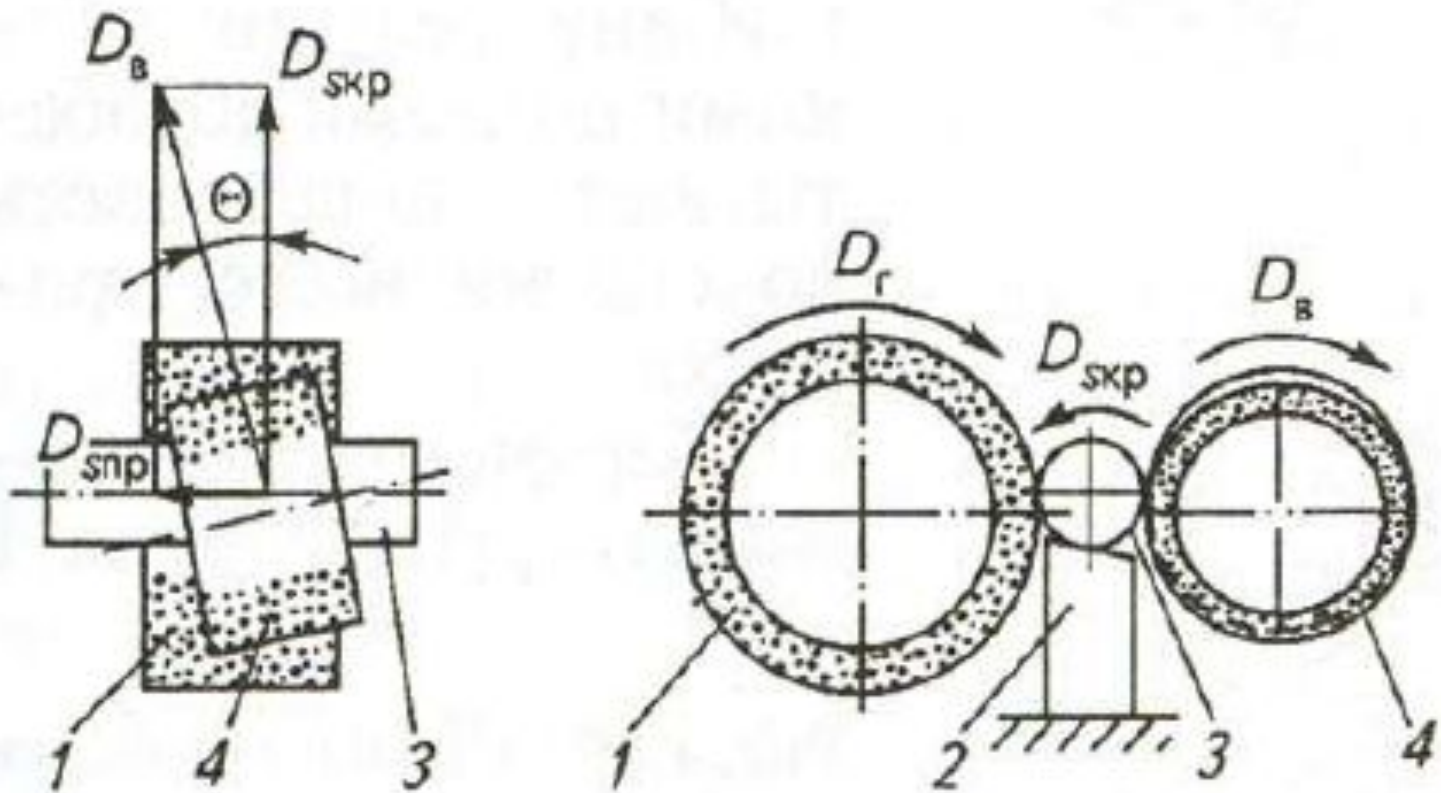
Схемы обработки заготовок на бесцентрово-шлифовальном станке:
